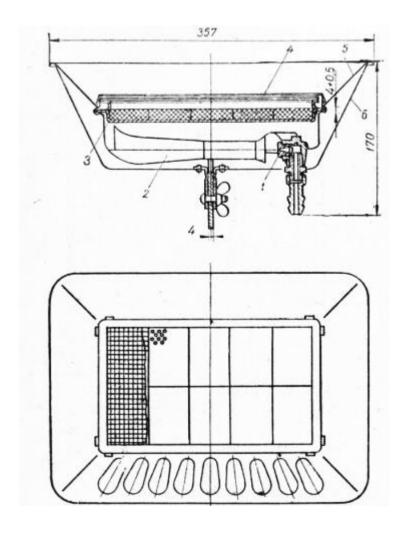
Горелка инфракрасного излучения ГИИВ-1 конструкции СКВ Газприбор-автоматика: 1 — форсунка; 2 — корпус; 3 — керамическая насадка; 4 — сетка; 5 — рефлектор; 5 — кожух; 7 — отверстие для поступления воздуха в корпус
